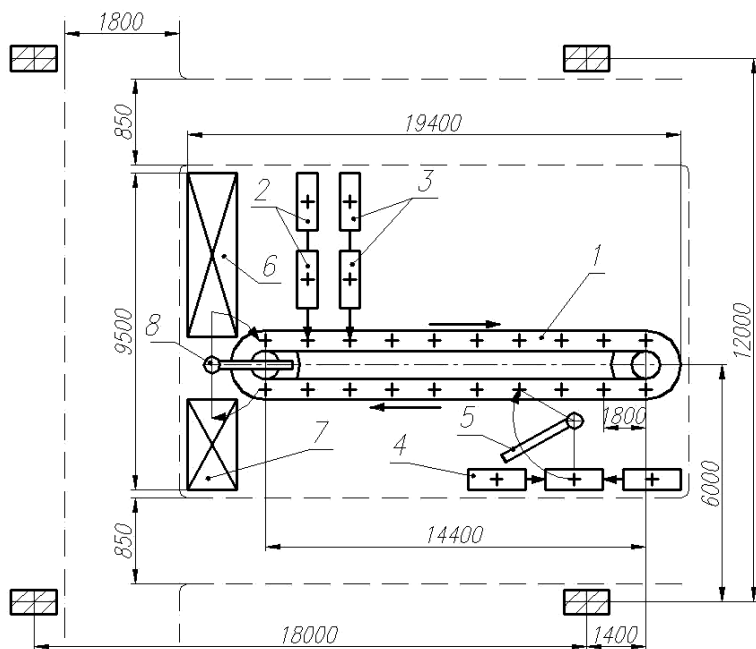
Компоновочная схема участка поточной сборки редуктора
